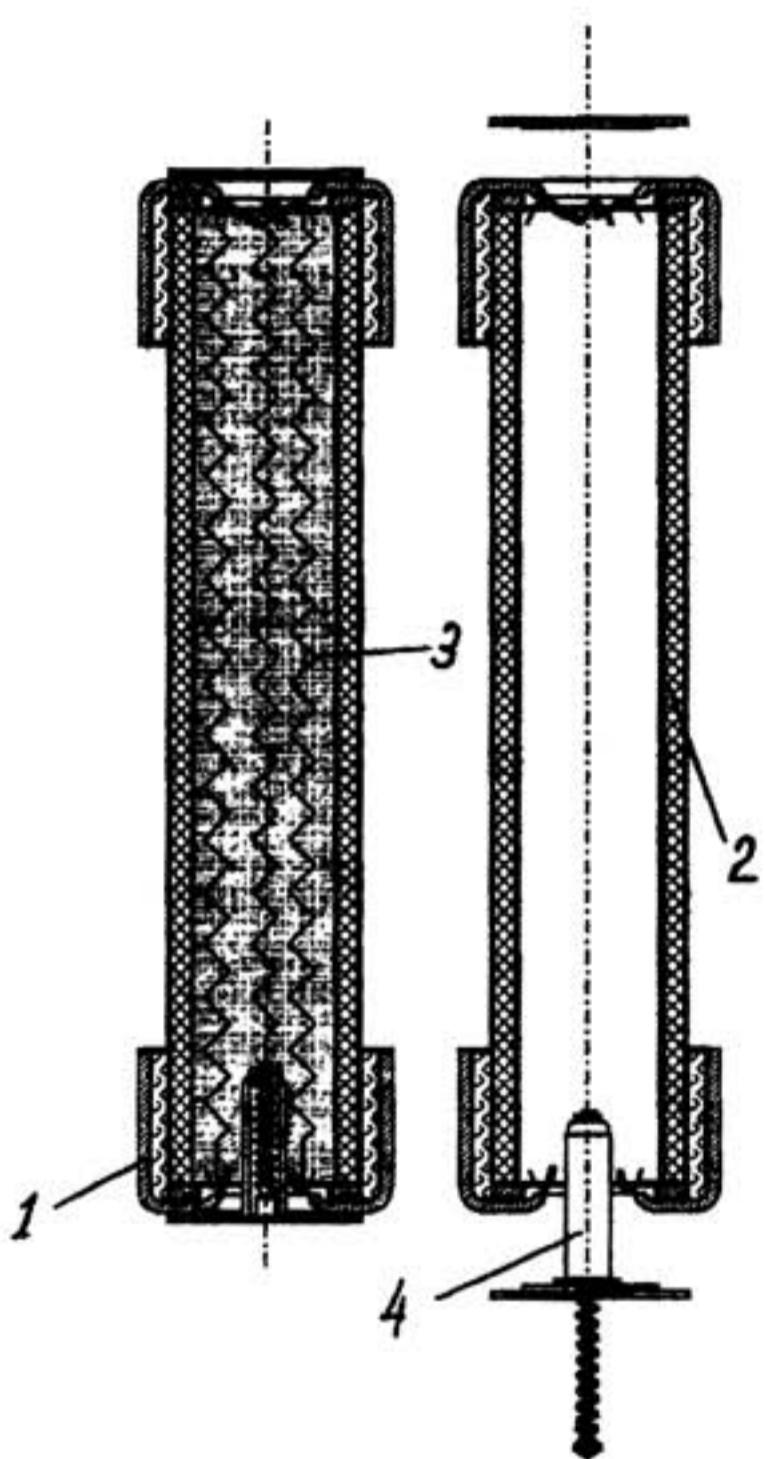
Кварцевый токоограничивающий предохранитель типа ПК на напряжение 10 кВ: 1 - металлический колпачок; 2 - фарфоровая трубка; 3 - вставки; 4 - указатель срабатывания
